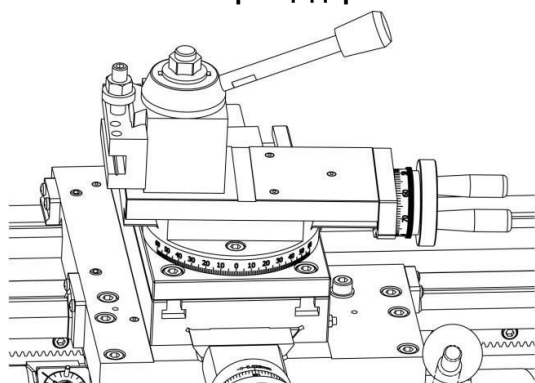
Опциональный резцедержатель быстрой смены инструмента
